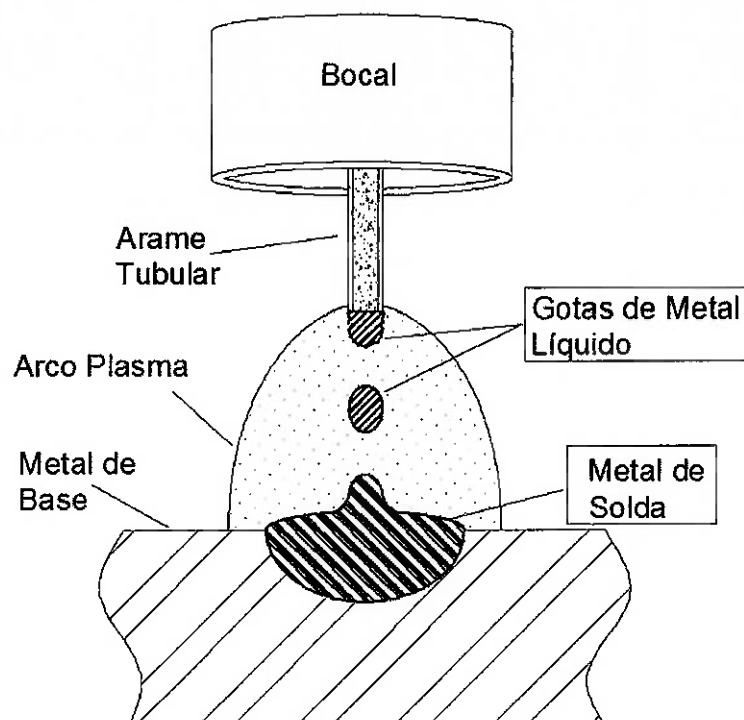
Esquema de soldagem que destaca o metal de solda e as gotas de metal líquido.
